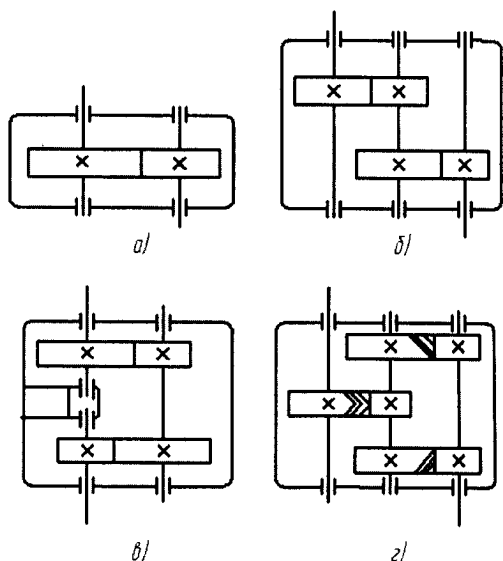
Принципові схеми циліндричних зубчастих редукторів
